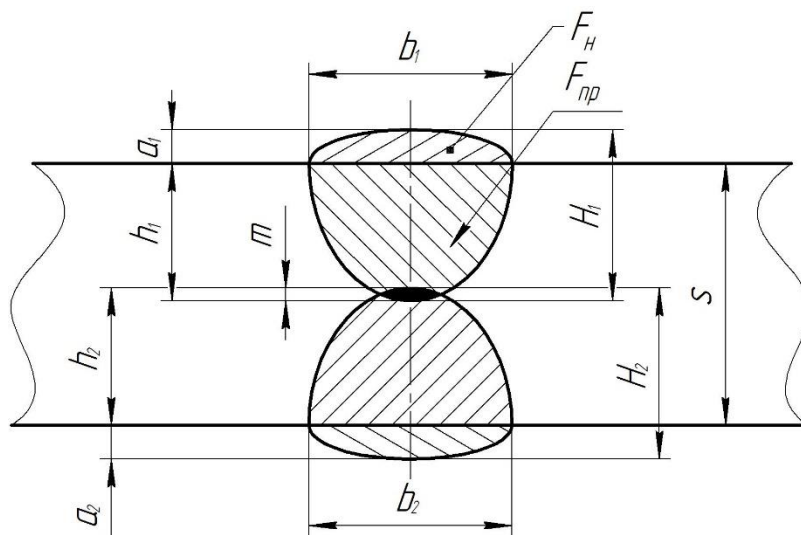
Основні геометричні розміри стикового шва при двобічному зварюванні
